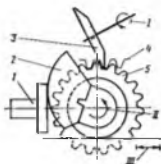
Схема шлифования зубчатых колес плоским кругом
